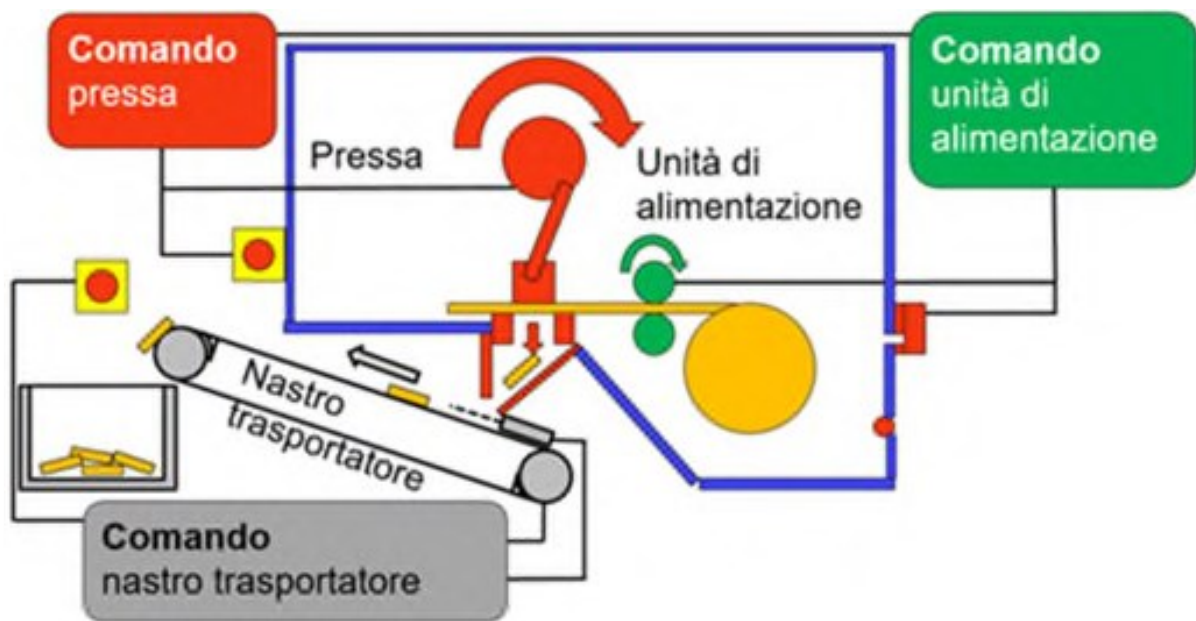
Schema di funzionamento dell'impianto pressa/alimentazione/nastro (da elaborato SUVA).
